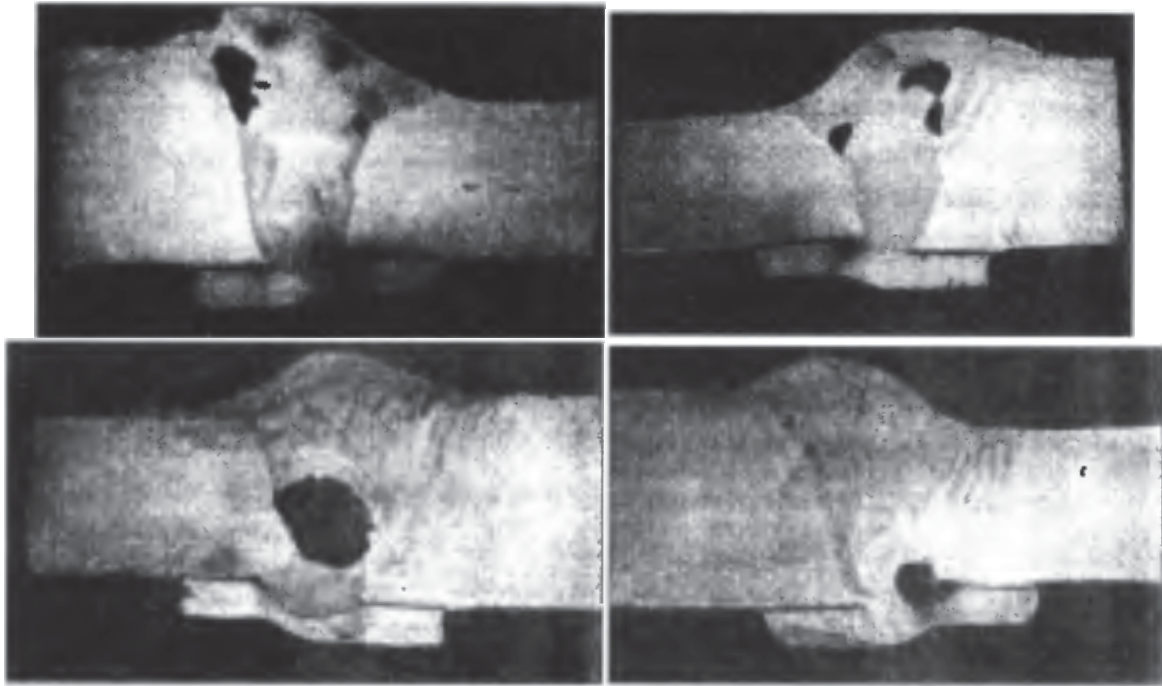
Поры в сварном шве (схемы):
